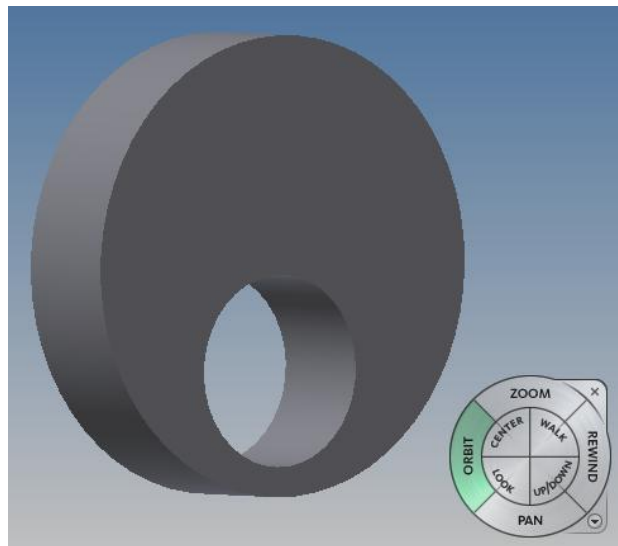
Diseño de la excéntrica en CAD Inventor Profesional.
